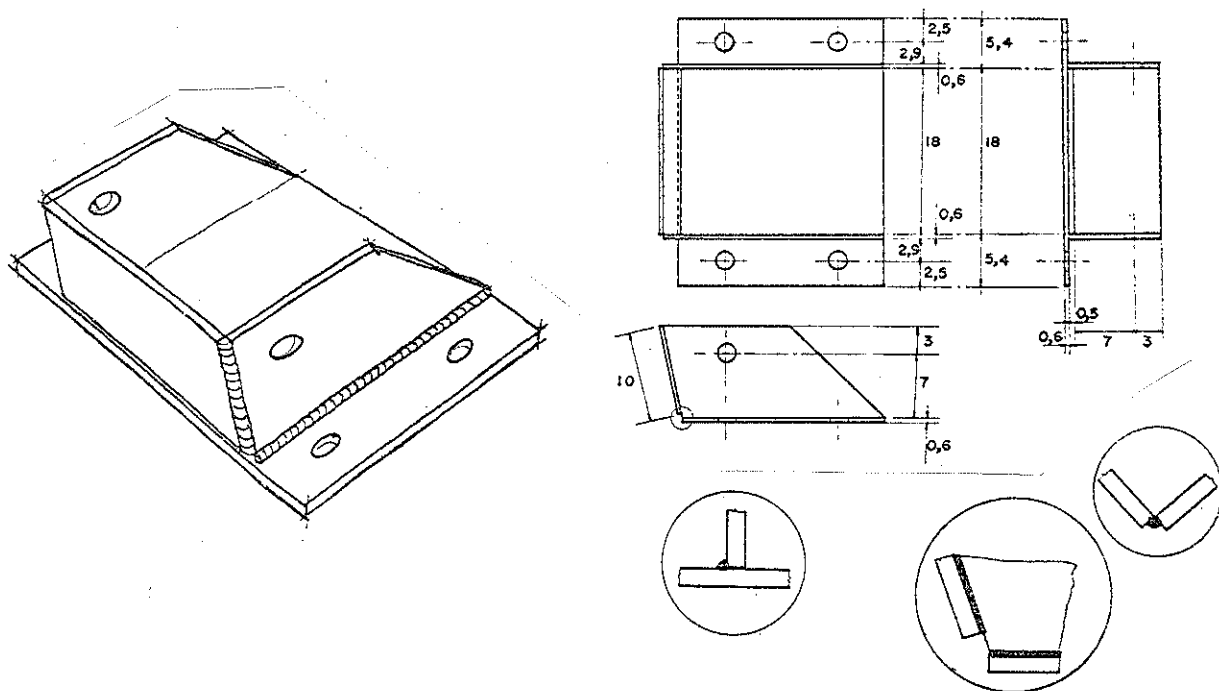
Placa de Apoio em Chapa Cortada e Soldada
